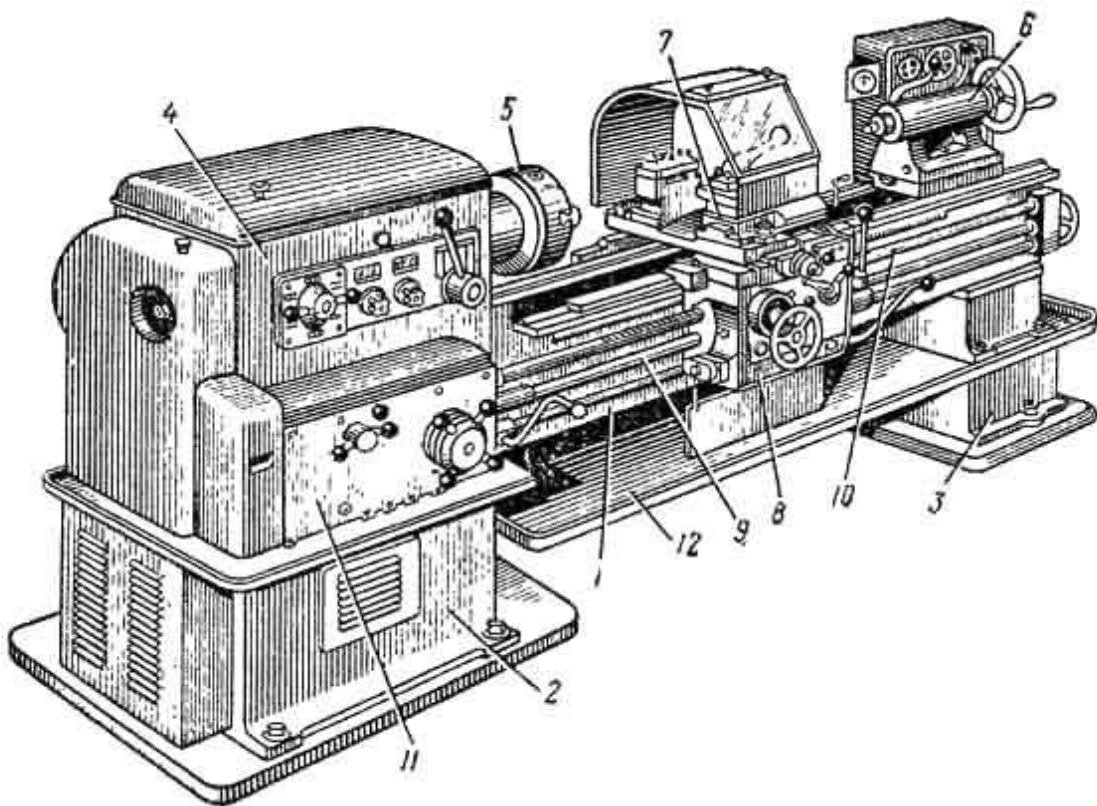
Загальний вигляд токарно-гвинторізного верстата 1К62.
